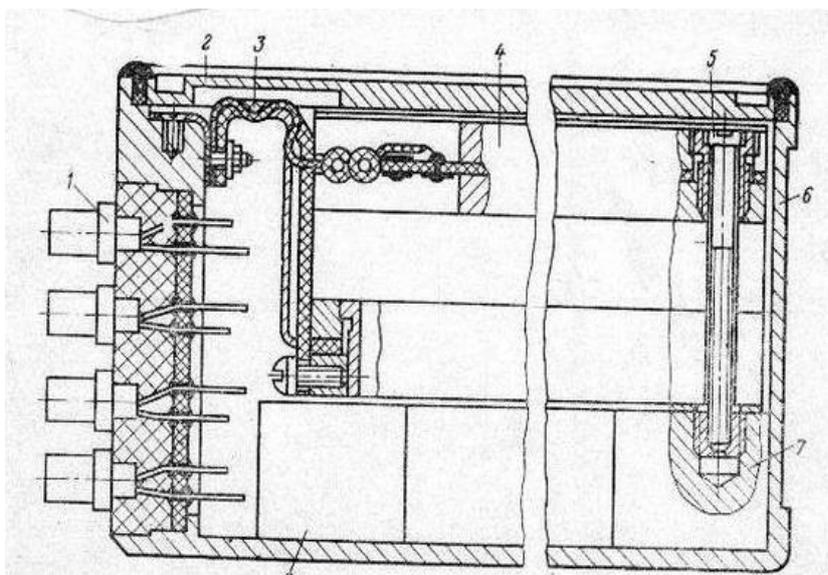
Книжная компоновка блока МЭА IV поколения:
